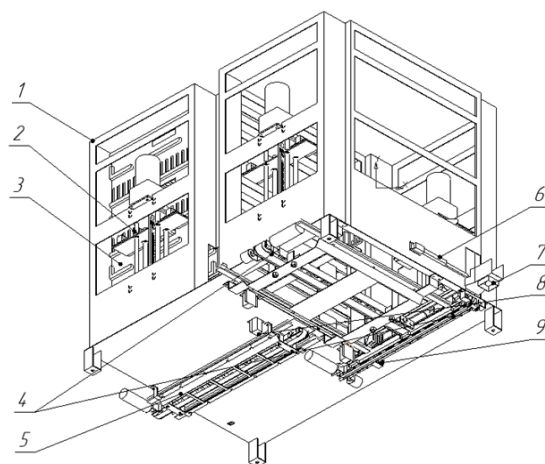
Устройство подачи рассады для посадочной машины: 1 — корпус устройства; 2 — подъемный механизм; 3 — контейнер; 4 — линейные приводы, предназначенные для разгрузки контейнера; 5 — линейный привод, перемещающий контейнеры; 6 — актуаторный привод заслонки контейнера; 7 — выход для рассады и направляющих; 8 — электромеханический замок; 9 — актуаторный подъемный механизм привода
